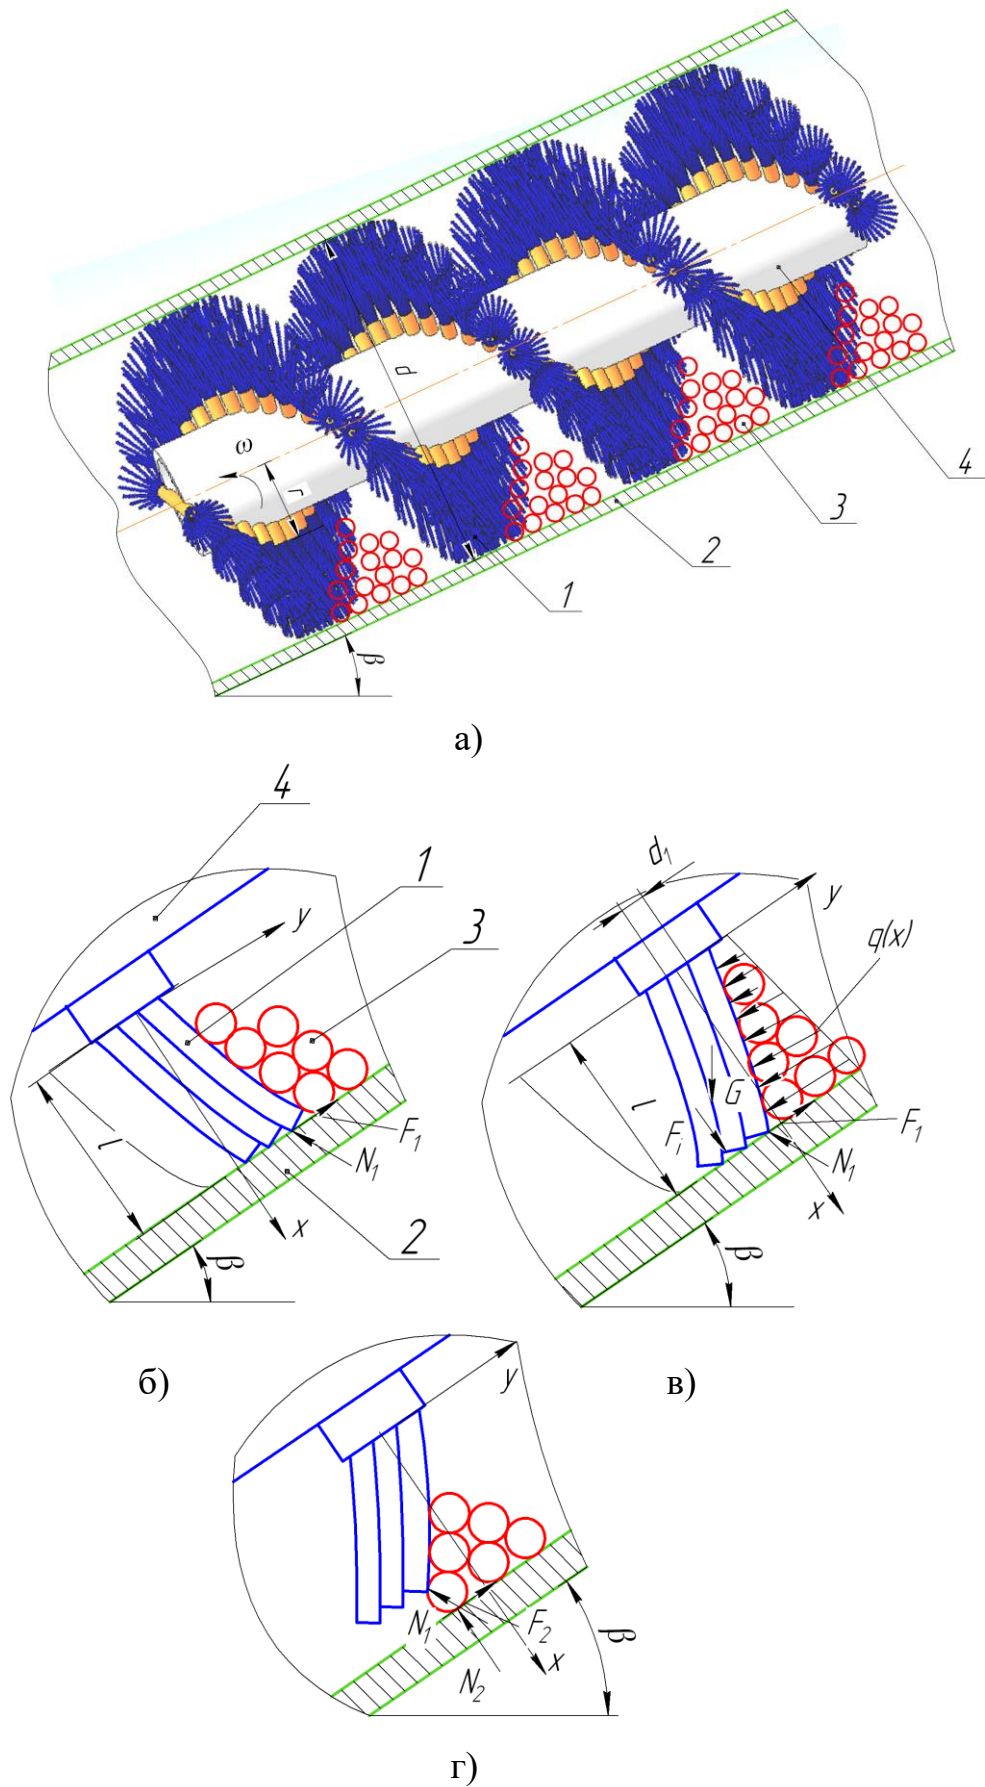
Розрахункова схема для визначення деформації еластичними щіткоподібними гвинтовими робочими органами при транспортуванні сипких матеріалів: 1 - ЕЩГРО; 2 – кожух; 3 – сипкий матеріал; 4 – вал
